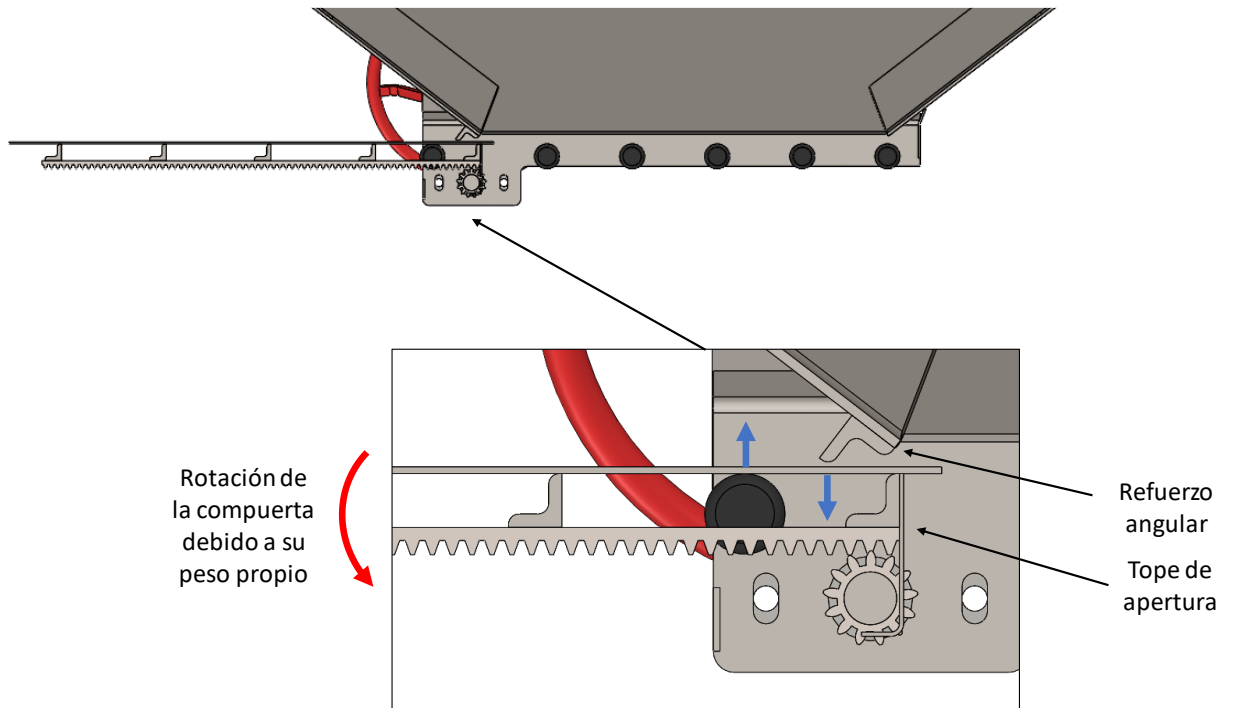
Corte y detalle del mecanismo de apertura.
